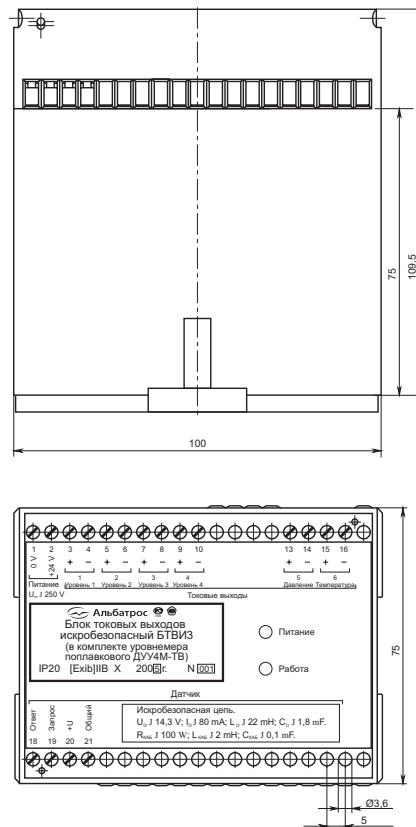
Габаритные размеры БТВИЗ
